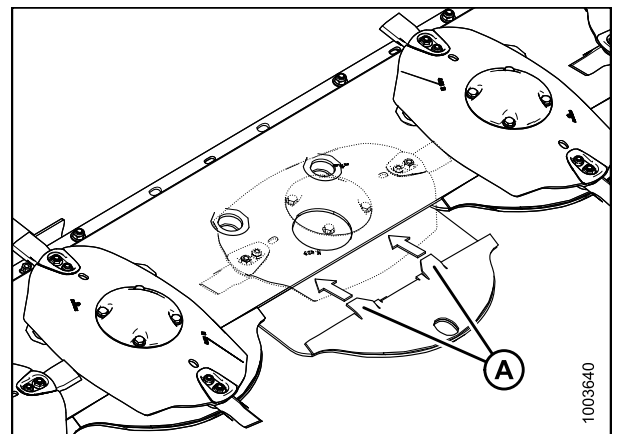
Jupe pare-pierres installée sur la barre de coupe
